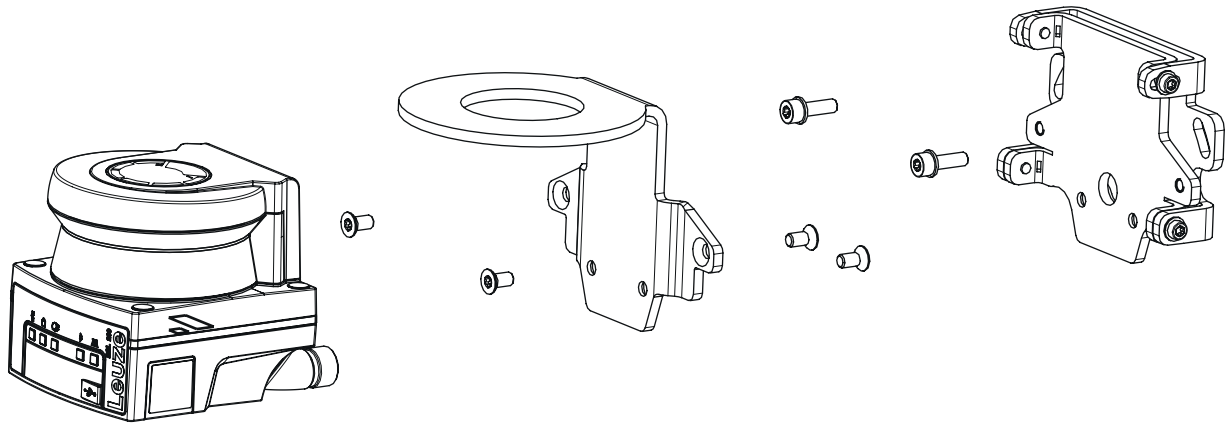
Montaggio con supporto a parete e staffa di protezione
